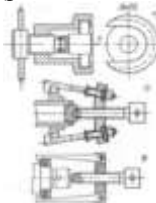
Винтовые упорные съемники: а - с захватом детали корпусом съемника; б, в - с захватом детали лапками
